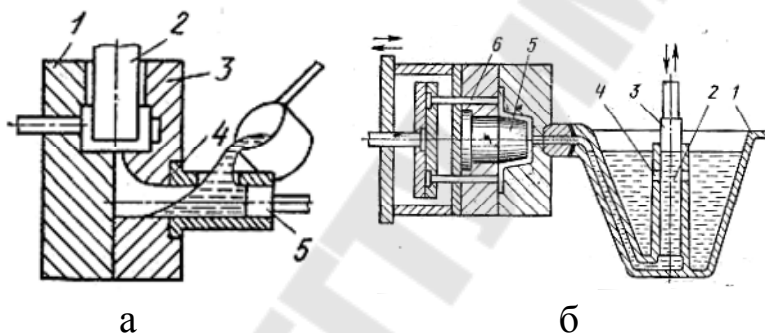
Схемы изготовления отливок литьем под давлением:
